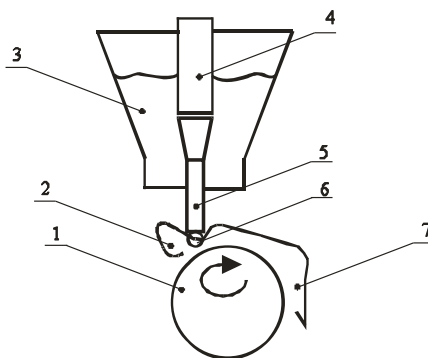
Схема автоматичного наплавлення: 1 - наплавлювана деталь; 2 - еластична оболонка; 3 - бункер з флюсом; 4 - мундштук; 5 - електрод; 6 - електрична дуга; 7 - шлакова кірка.
